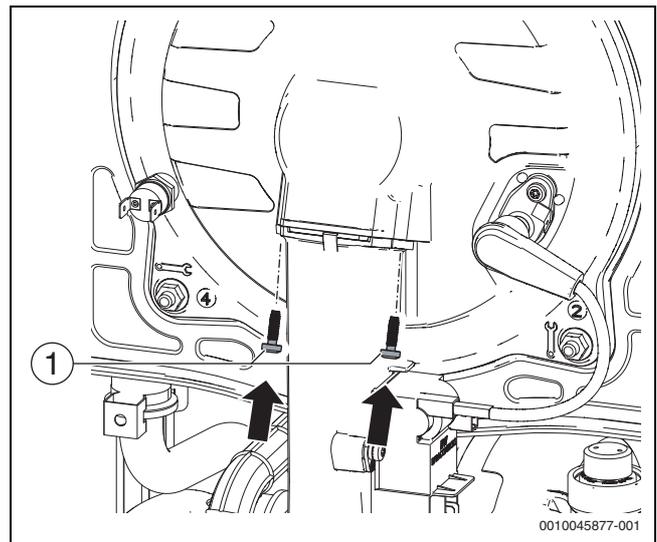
Montaje del tubo de aire-gas en la puerta de la cámara de combustión
